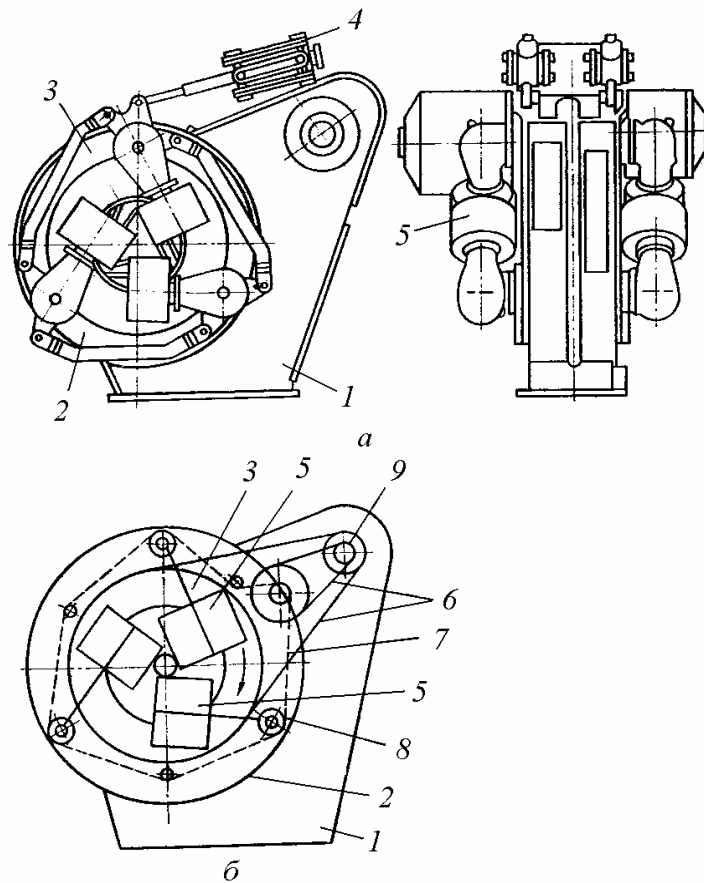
Роторный окорочный станок ОК-35М: *a* – общий вид; *б* – кинематическая схема привода; 1 – станина; 2 – статор; 3 – ротор; 4 – прижим вальцов; 5 – питающие вальцы; 6 – клиноременная передача; 7 – цепная передача; 8 – коническая зубчатая передача; 9 – ведущий вал
